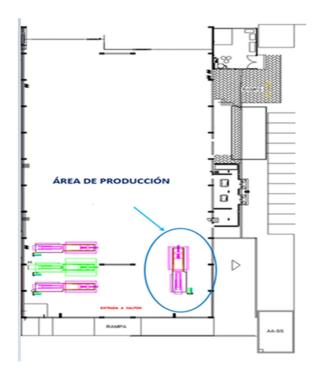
Esquema donde irá ubicado el equipo en la Planta Fuente: (Plastigama Wavin, 2019)
